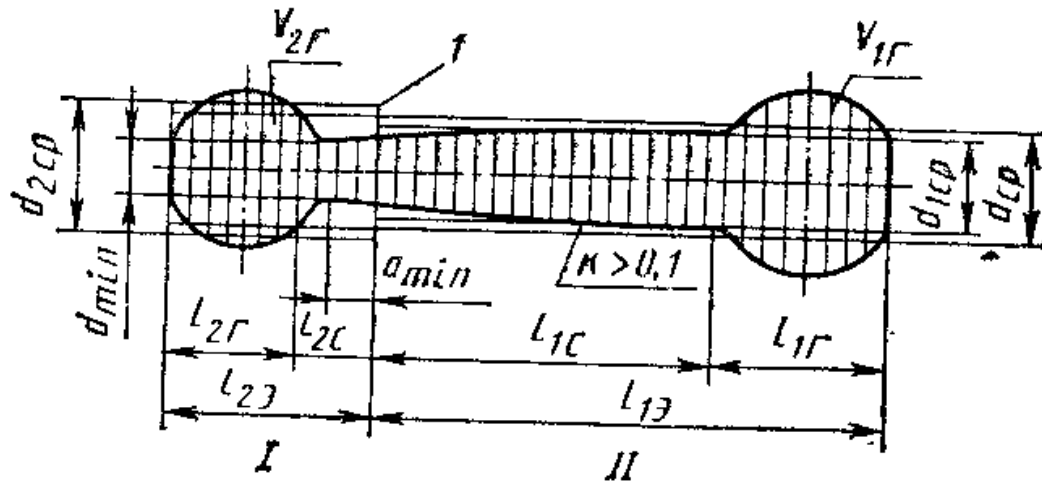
Приведення складної заготовки (епюри) дві головки – стрижень до елементарних розрахункових заготовок для випадку коли стрижень має значний ухил (1 – лінія розділу)
